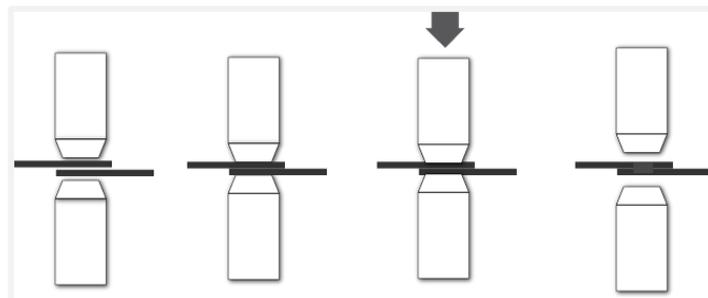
Secuencia en el proceso de soldadura de punto por resistencia.
